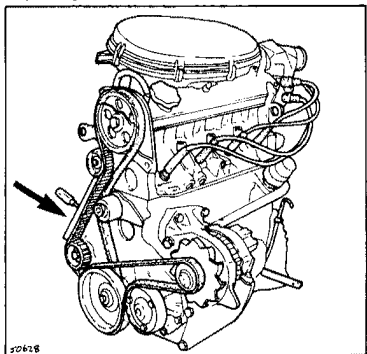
Стрелки на зубчатом ремне должны быть расположены между зубчатым шкивом промежуточного вала и шкивом натяжителя
